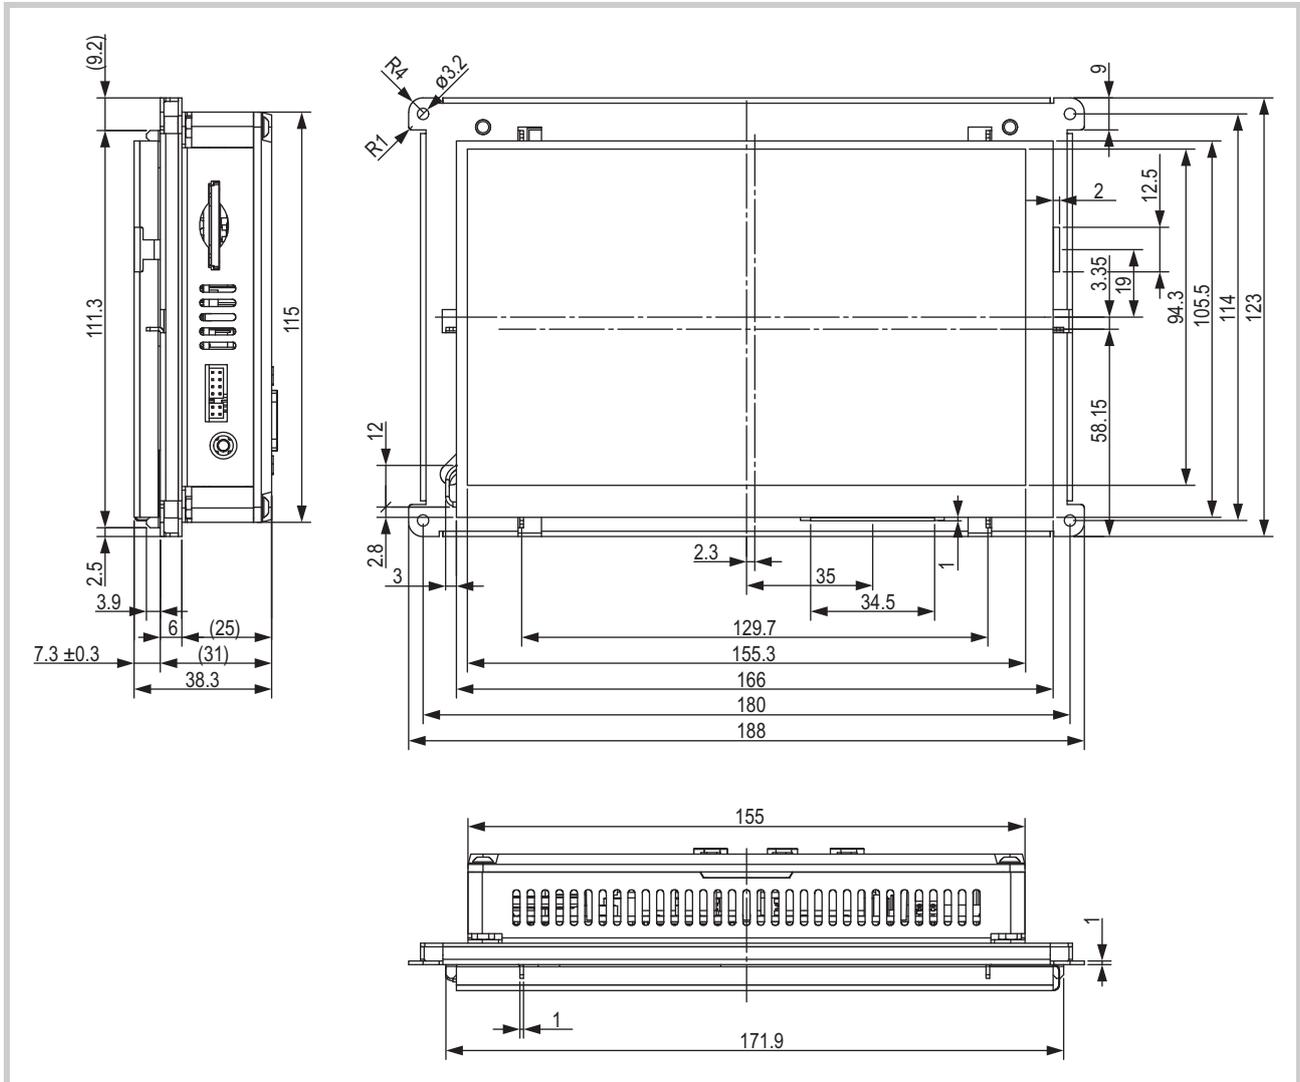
Mechanische Abmessungen der 7,0"-Geräte in mm
